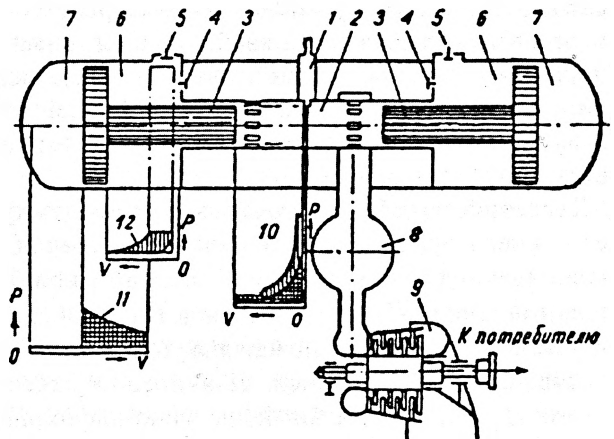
Схема двигателя профессора А. Н. Шелеста со свободнопоршневым генератором сжатых газов
